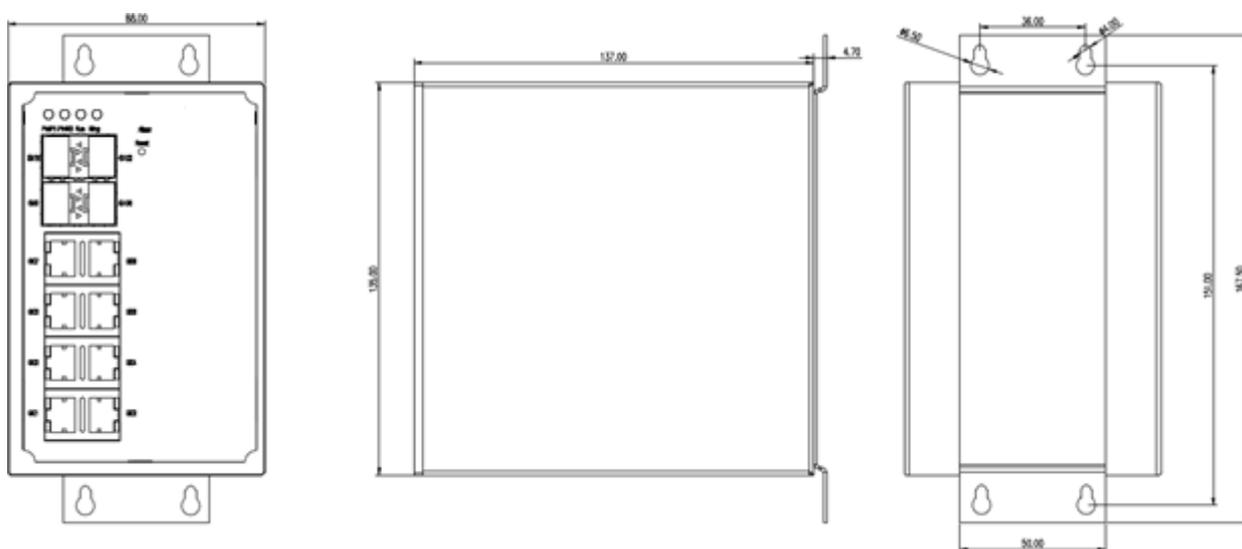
Габаритный чертеж корпуса «Тип 2» с креплением на плоскую поверхность
